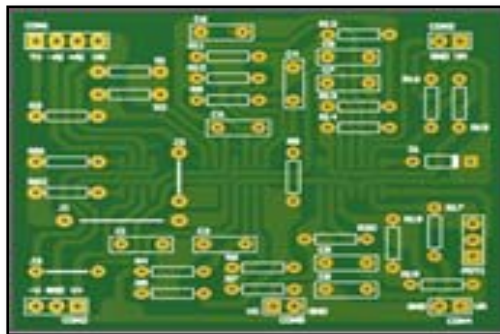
Diseño PCB de la Tarjeta sEMG.
